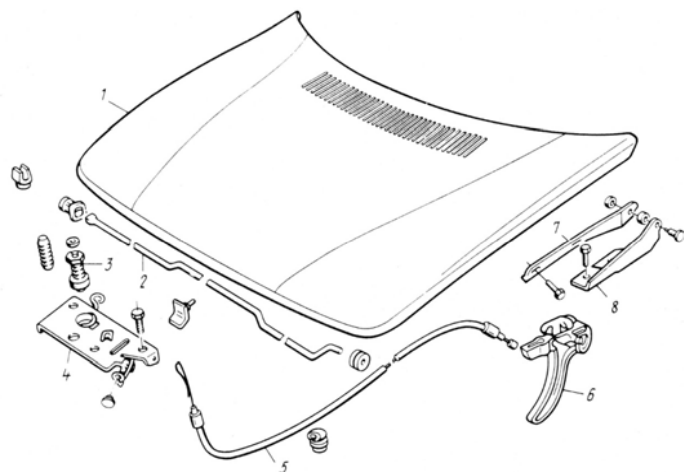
Капот двигателя автомобиля с механизмом открывания:
